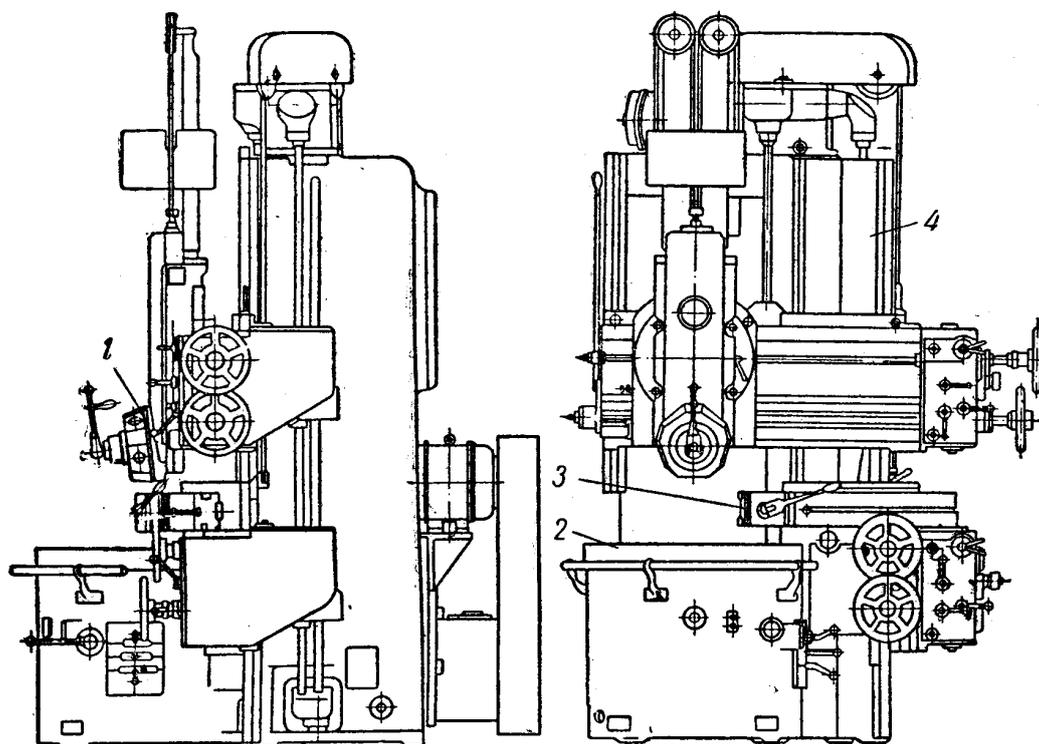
Общий вид токарно-карусельного станка: 1 – вертикальный суппорт; 2 – планшайба; 3 – боковой суппорт; 4 – стойка
